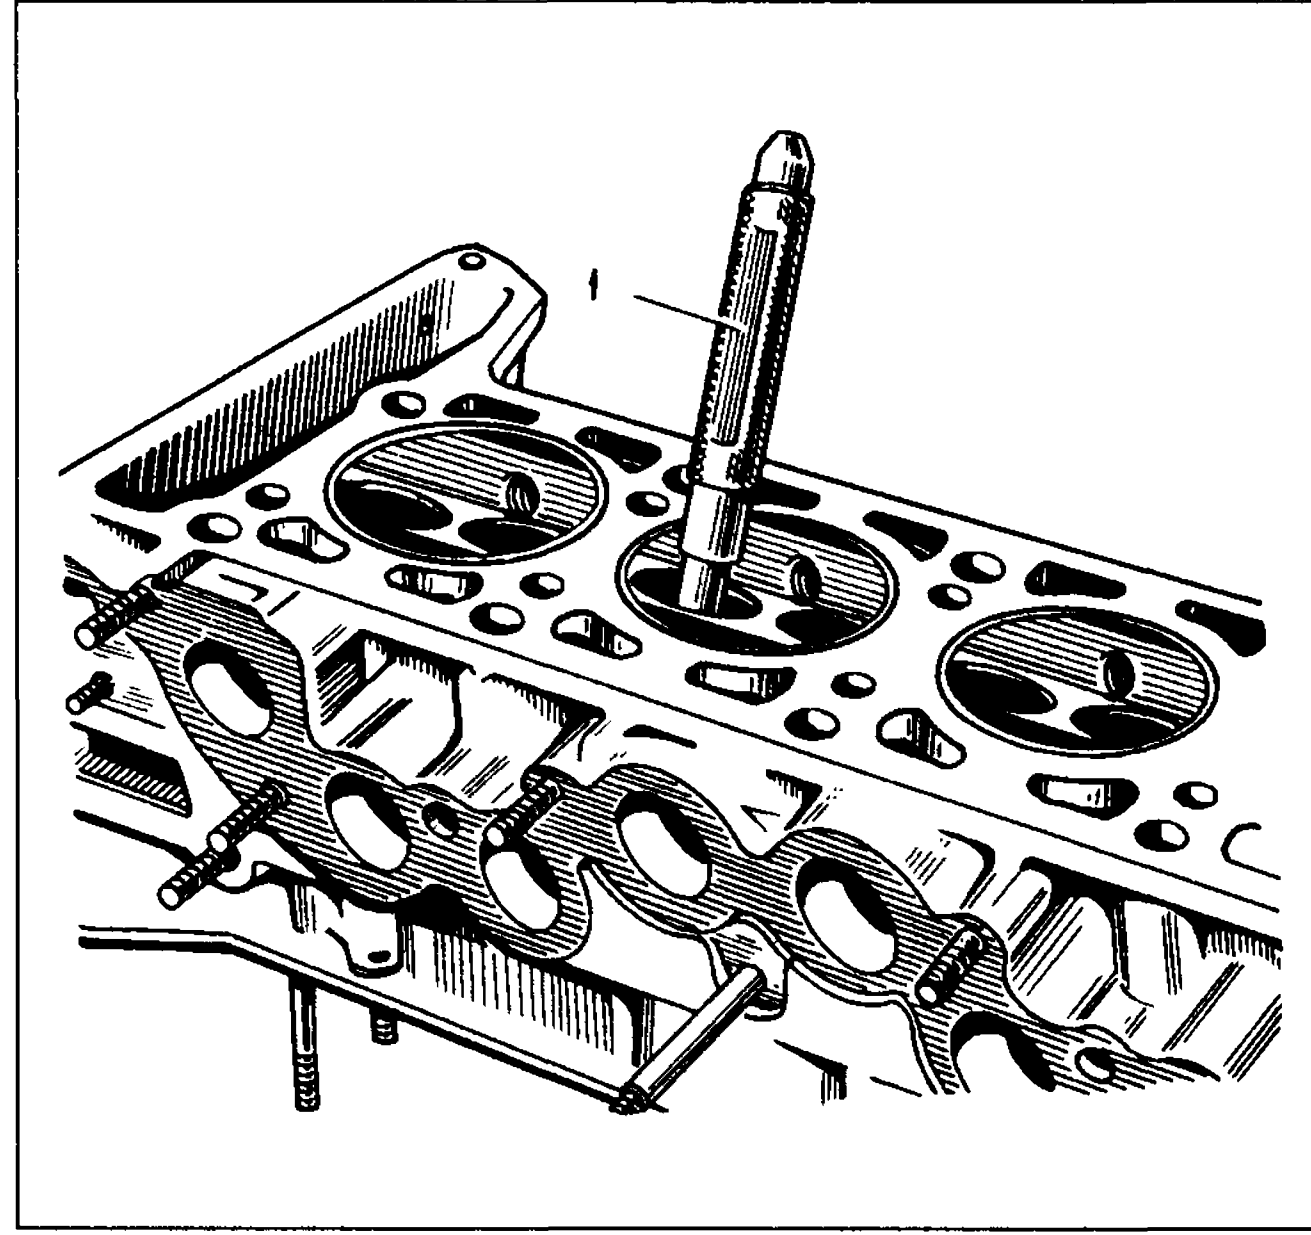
Выпрессовка направляющих втулок клапанов: 1 - оправка А.60153/R
